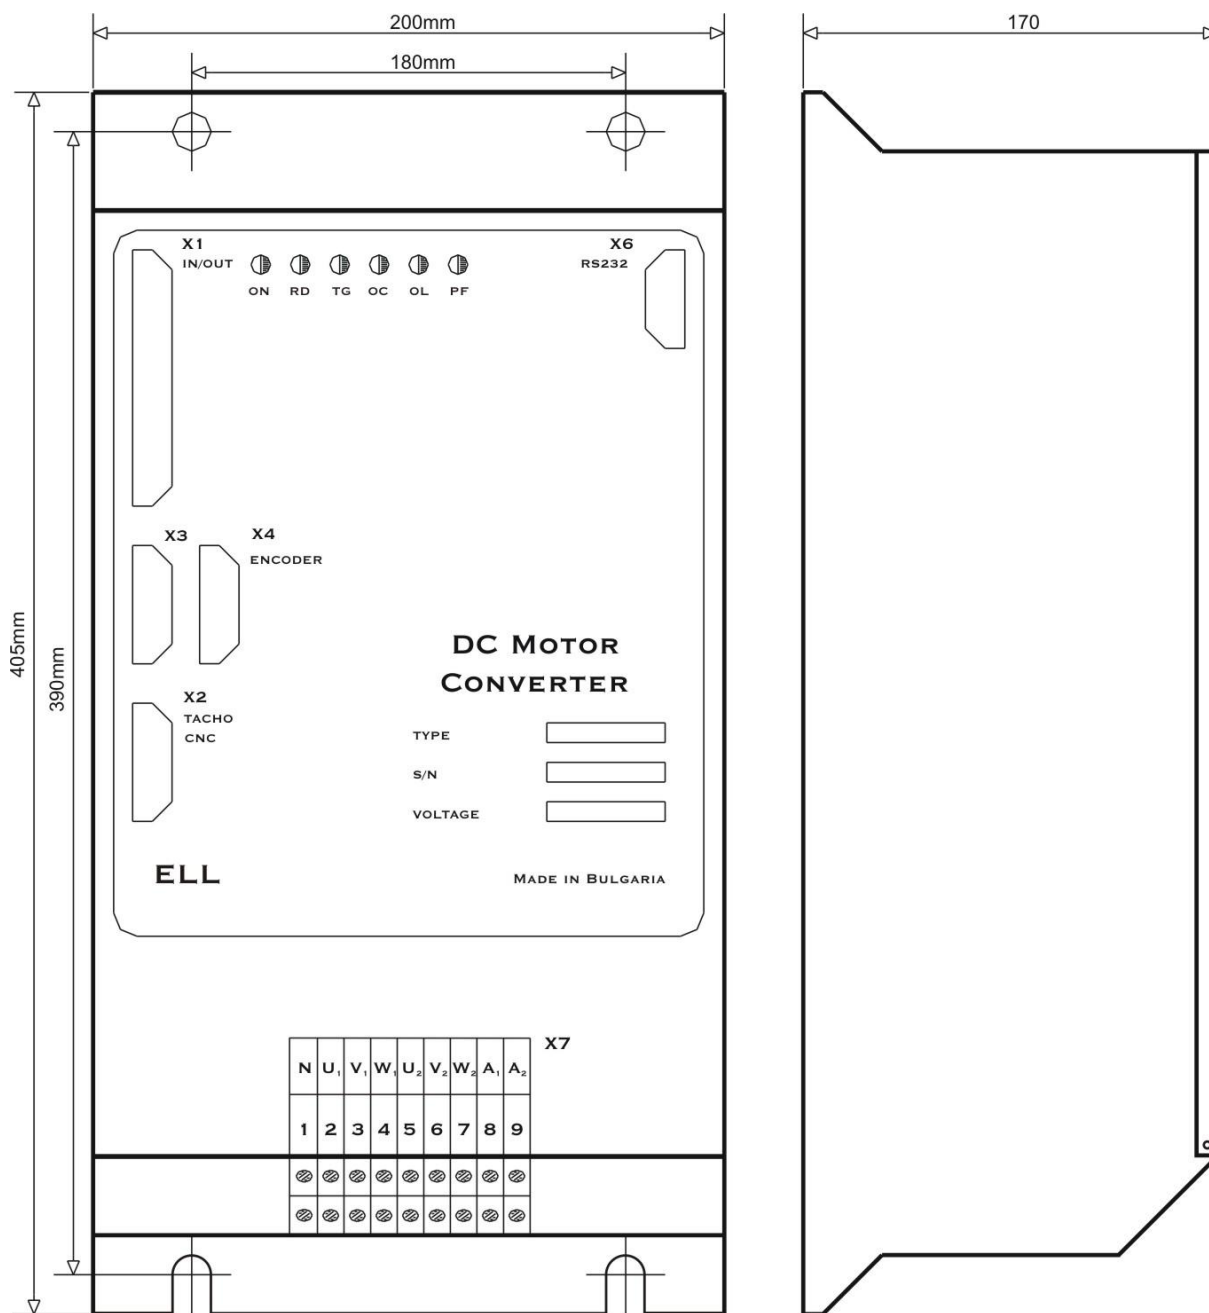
Присоединительные и габаритные размеры преобразователей типов 12XXX/400
